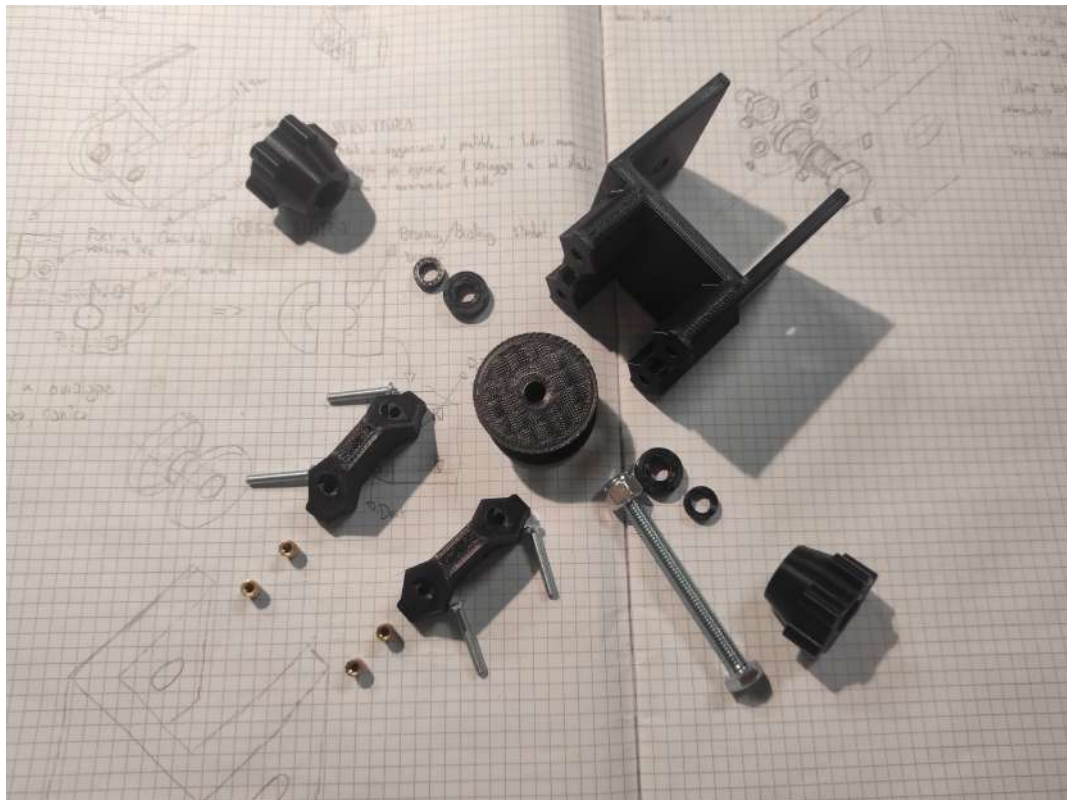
Esploso di un tensionatore prima di essere assemblato.
